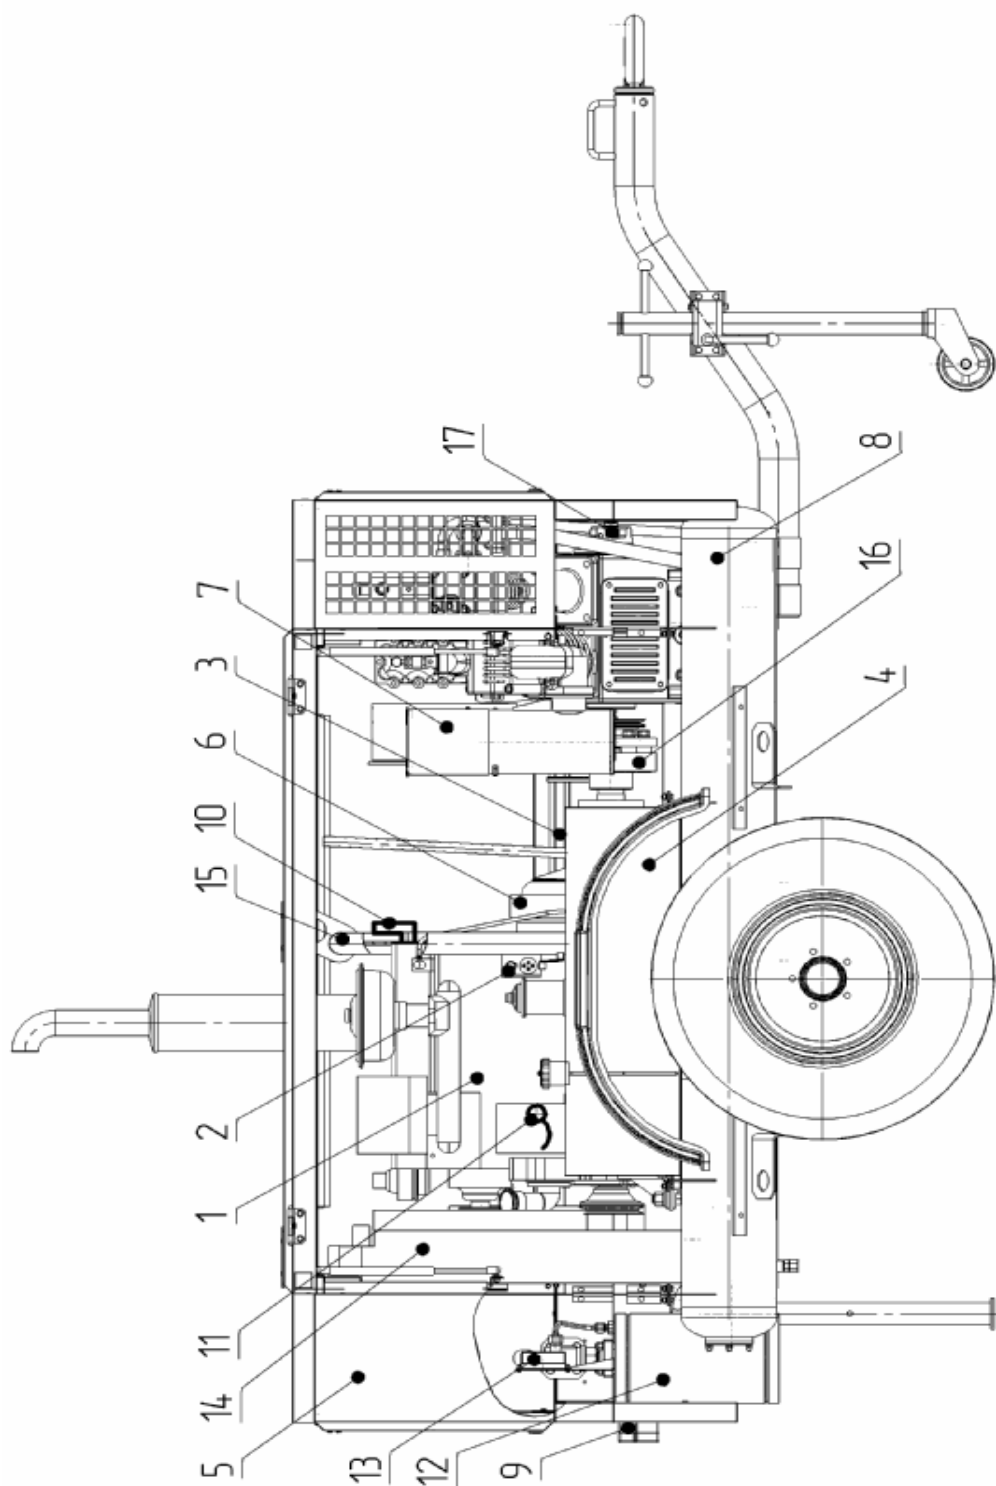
Передвижная компрессорная станция типа ПКСД-1,4/25 (ПКСД-1,5/16)
